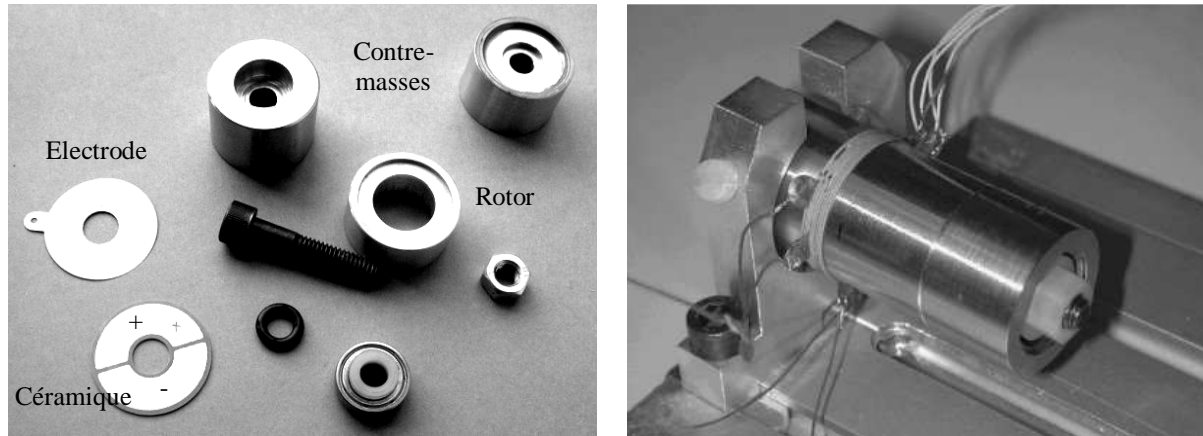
Vue éclatée et assemblée d'un moteur à rotation de mode
